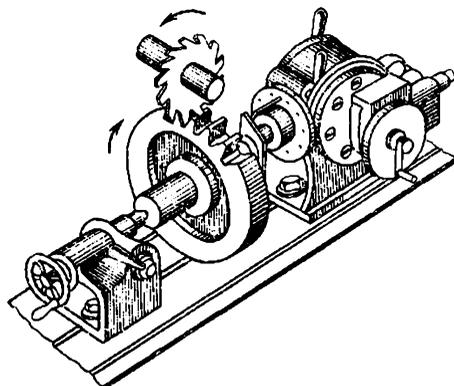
Нарезание зубьев зубчатых колес дисковыми фрезами
